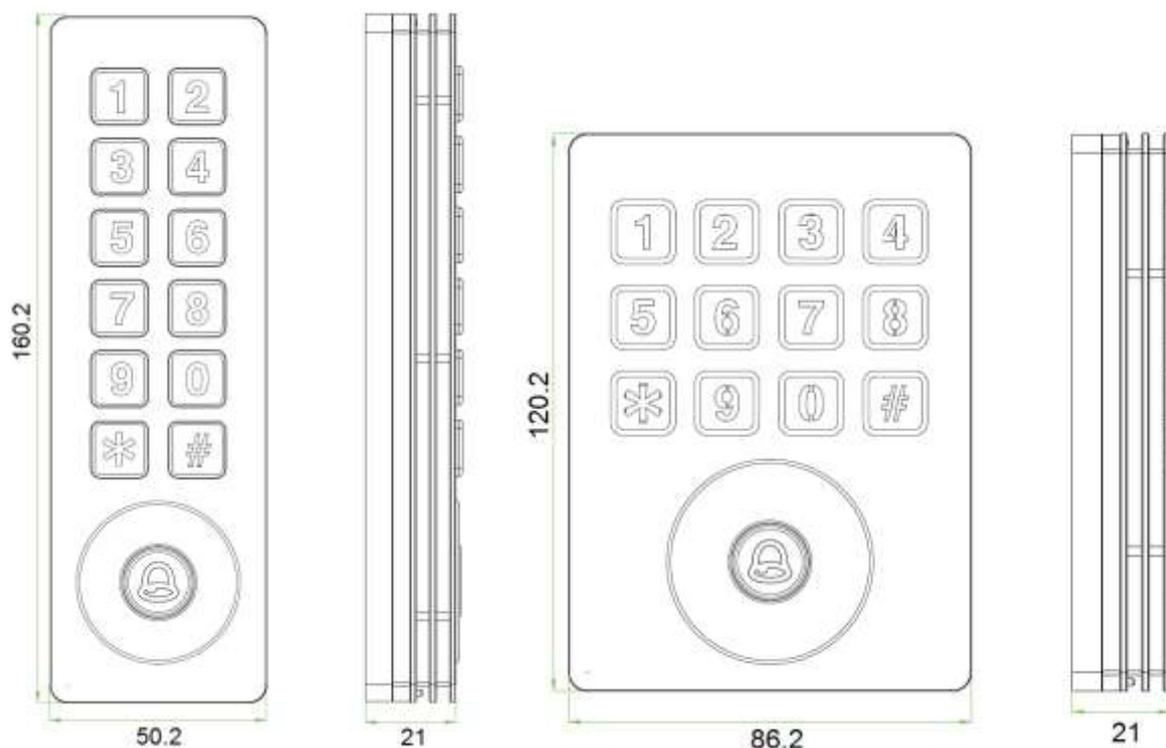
Внешний вид и габаритные размеры контроллеров
